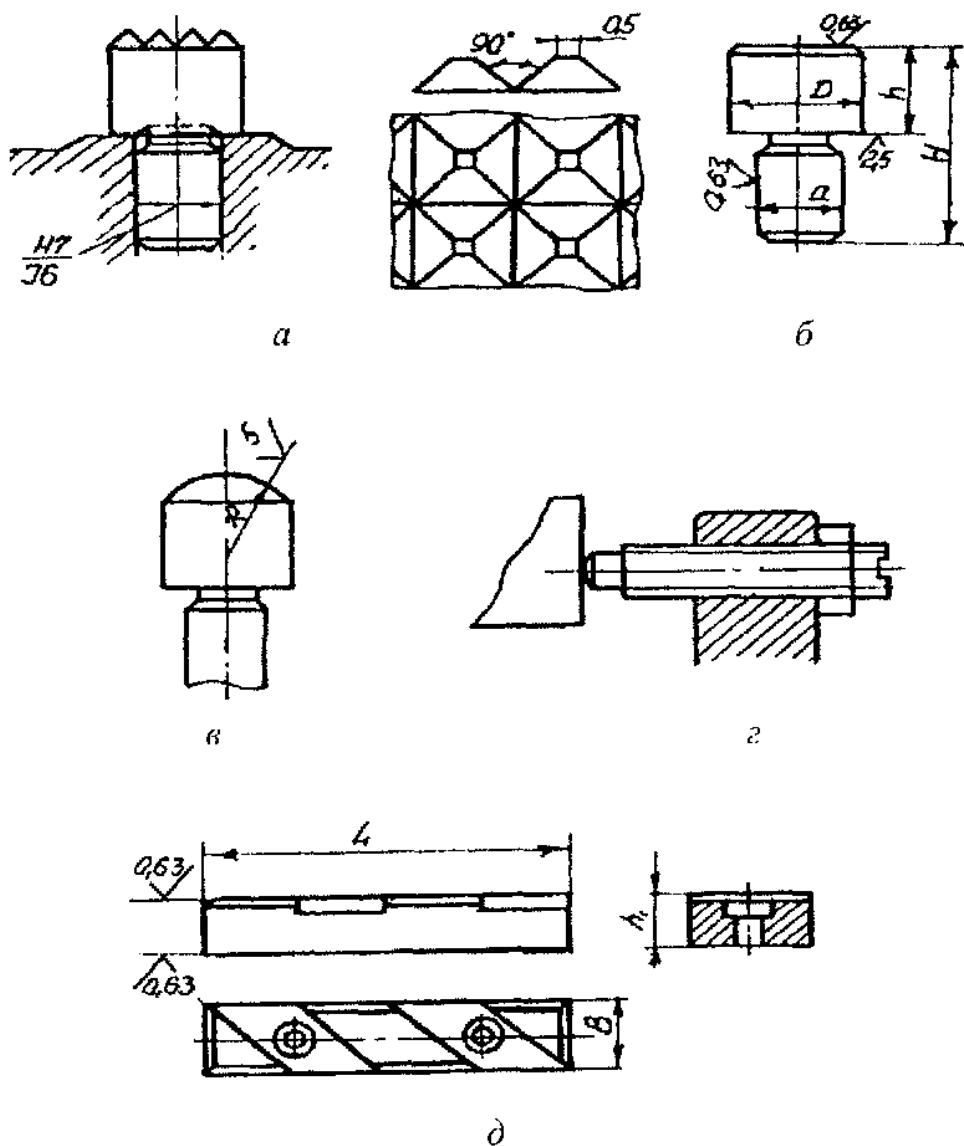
Схеми опор для встановлення на плоскі поверхні
